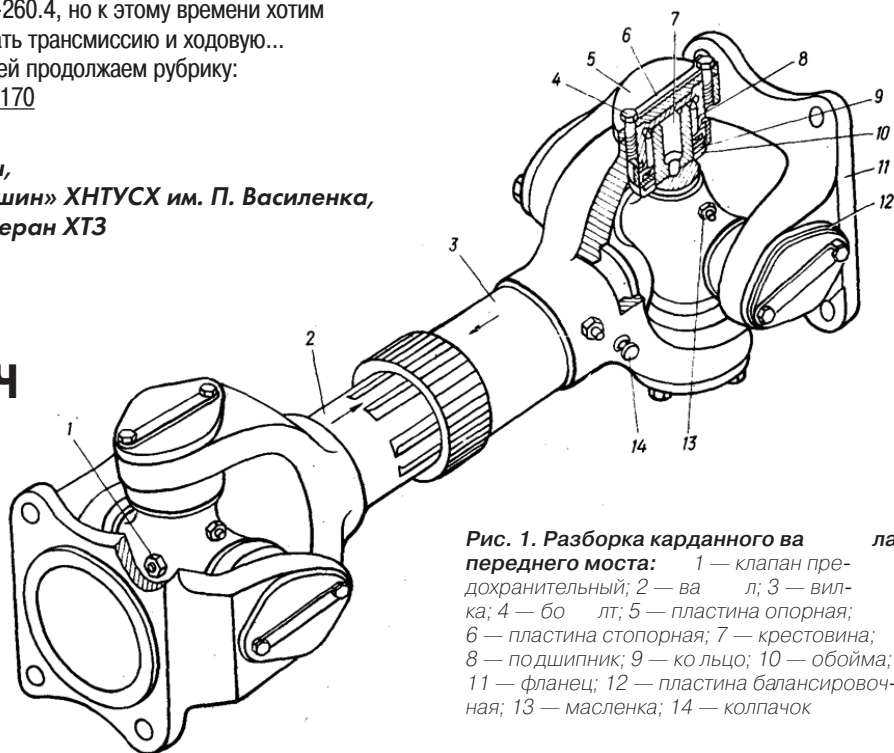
Разборка карданного вала переднего моста: 1 — клапан предохранительный; 2 — вал; 3 — вилка; 4 — болт; 5 — пластина опорная; 6 — пластина стопорная; 7 — крестовина; 8 — подшипник; 9 — кольцо; 10 — обойма; 11 — фланец; 12 — пластина балансировочная; 13 — масленка; 14 — колпачок
